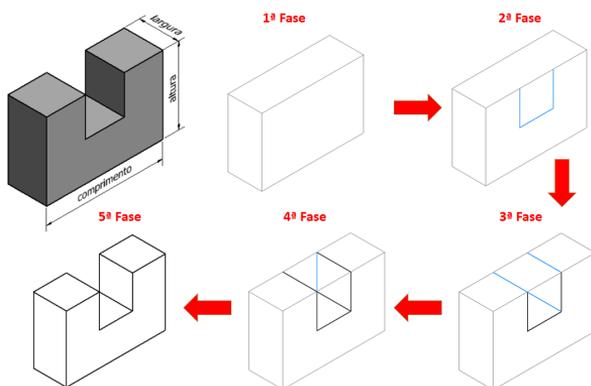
| Fases para construção de uma perspectiva: prisma com um rebaixo
